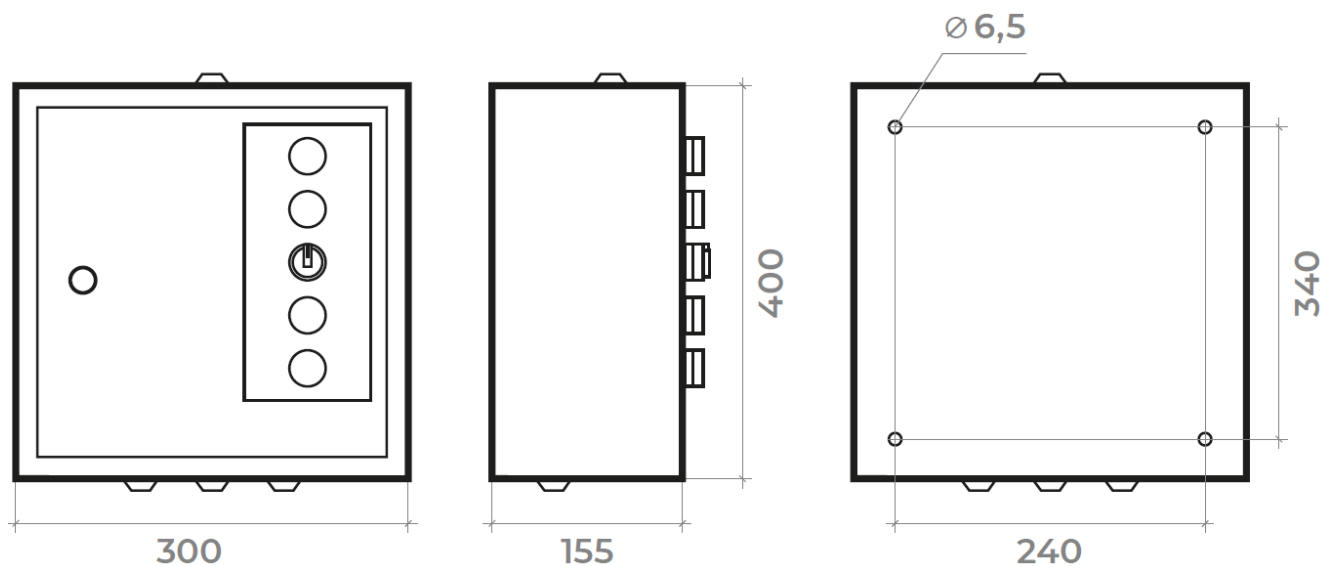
Габаритные и установочные размеры ШУВ-3/ШУВ-15.
